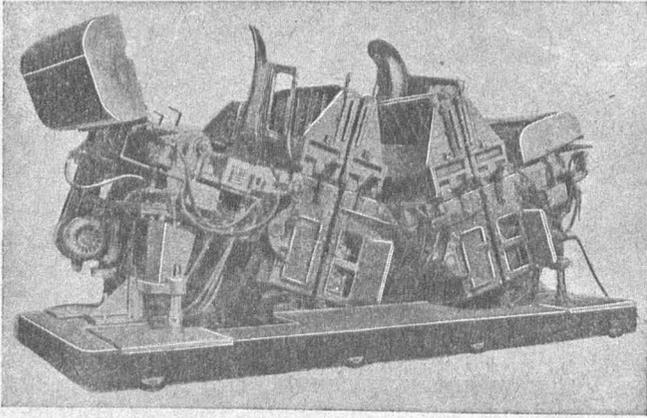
Стыковая машина для сварки боковин и задней стенки кузова автомобиля
